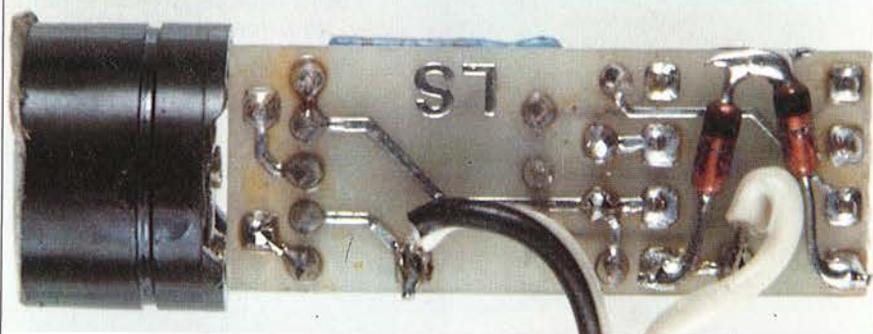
Alcuni componenti potranno essere montati anche sulla faccia inferiore del circuito stampato.
